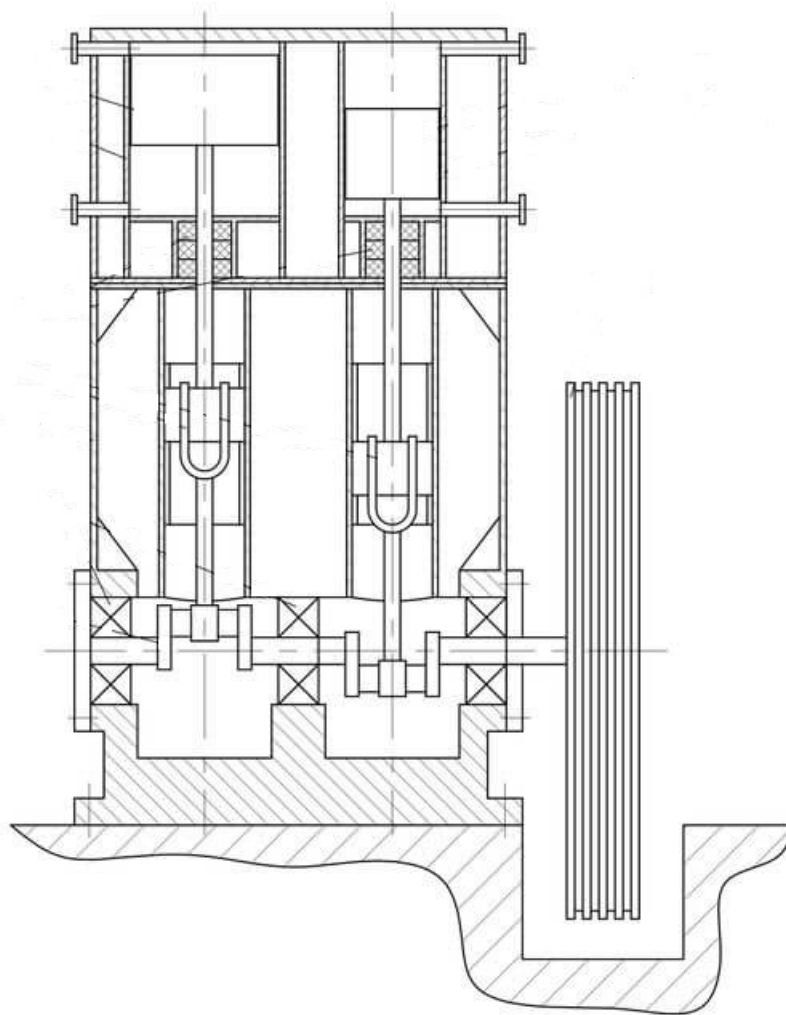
«Вертикальний дворядний двоступеневий компресор»
